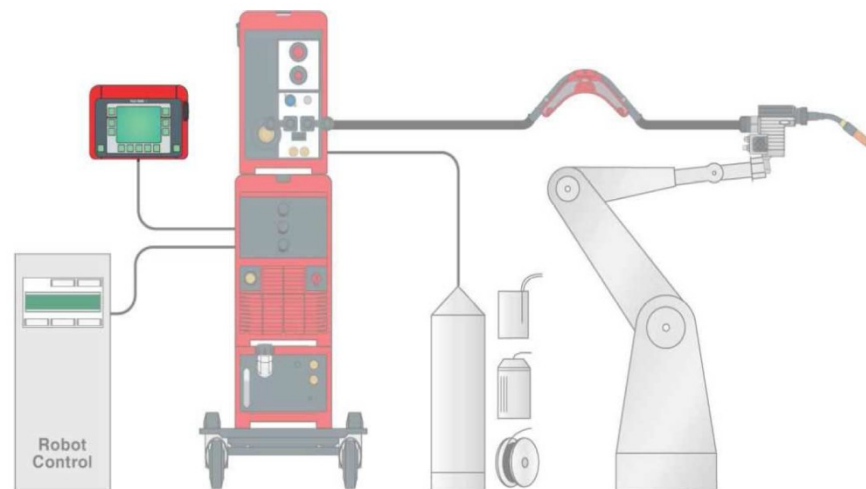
Ukázka mechanizovaného obloukového svařování [17]
